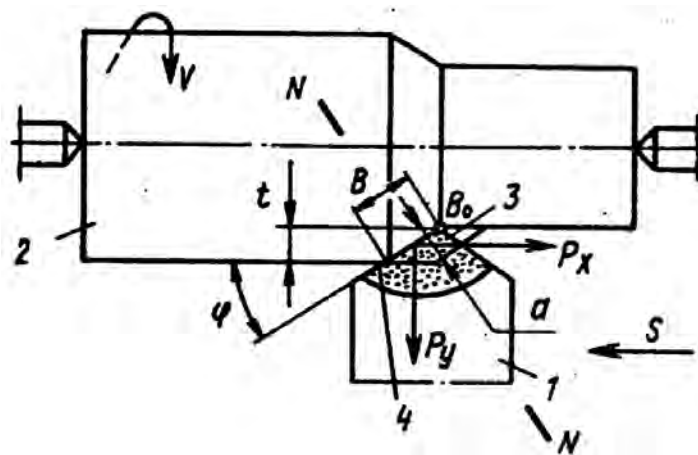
Схема обработки: 1 – резец; 2 – обрабатываемая деталь; 3 – сечение среза; 4 – главное режущее лезвие резца
